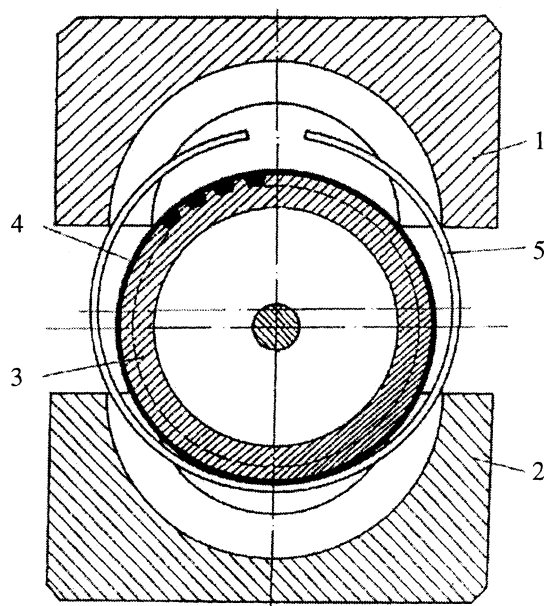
Схема универсальной пресс-формы для изготовления приводных ремней: 1, 2 – верхняя и нижняя полуформы; 3 – профильный барабан; 4 – заготовка; 5 – упругая втулка
